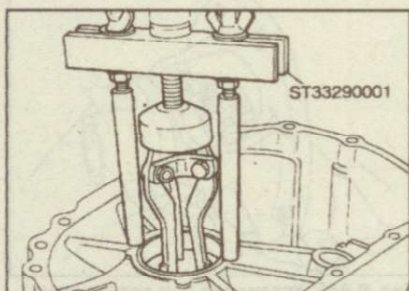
Снятие наружного кольца подшипника дифференциала (со стороны картера коробки передач)
